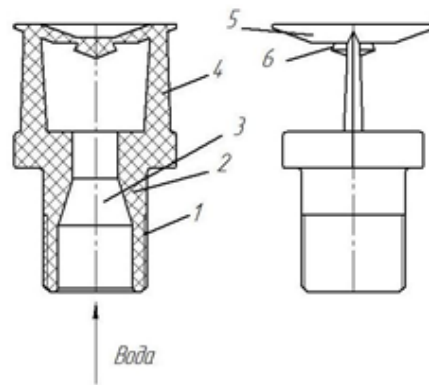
Предлагаемая дождевальная дефлекторная насадка: 1 – резьба; 2 – корпус; 3 – сопло; 4 – ножка дефлектора; 5 – дефлектор; 6 – канавка
